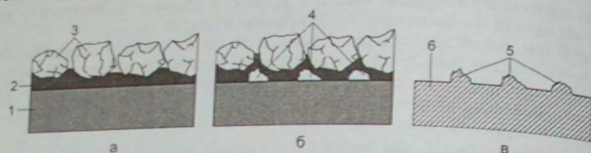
Схема образования поверхностных дефектов на рабочей поверхности КО и отливке
